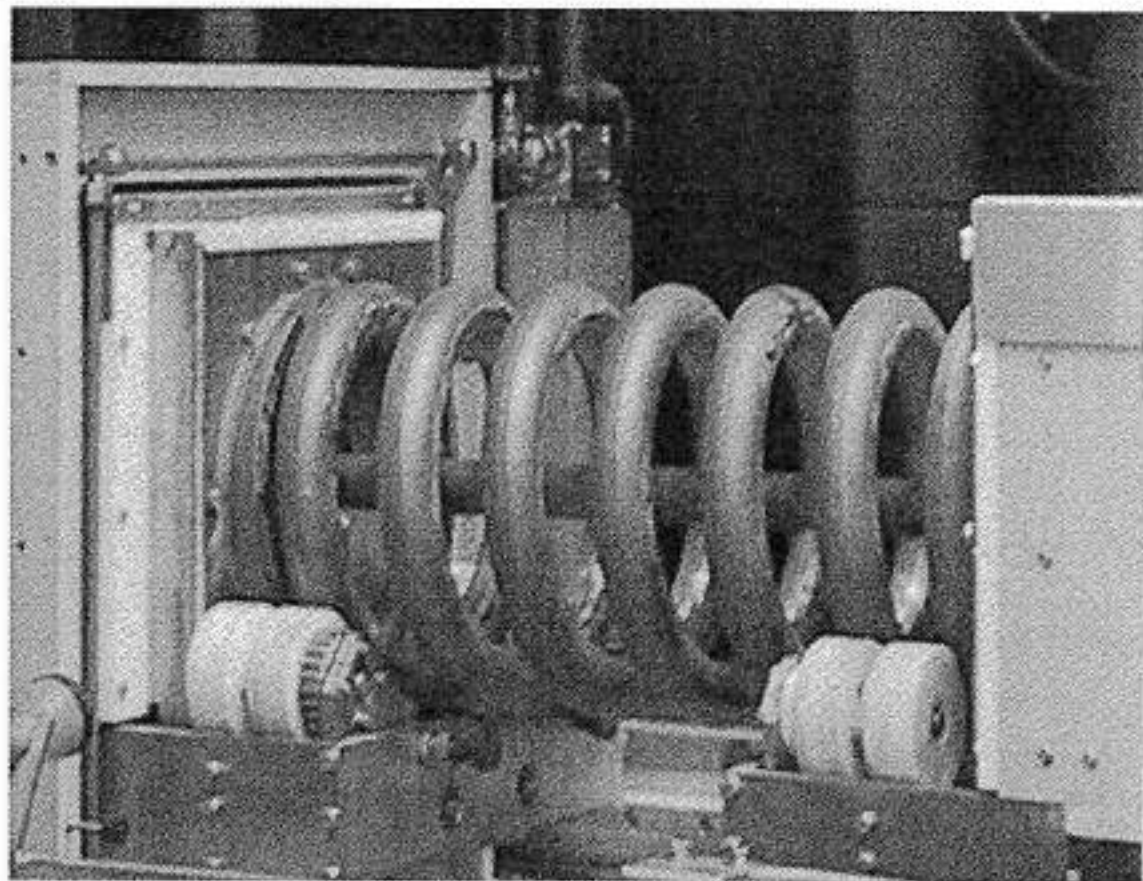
Проведение магнитопорошкового контроля пружины с помощью дефектоскопа CRAFTTEST SPRING
